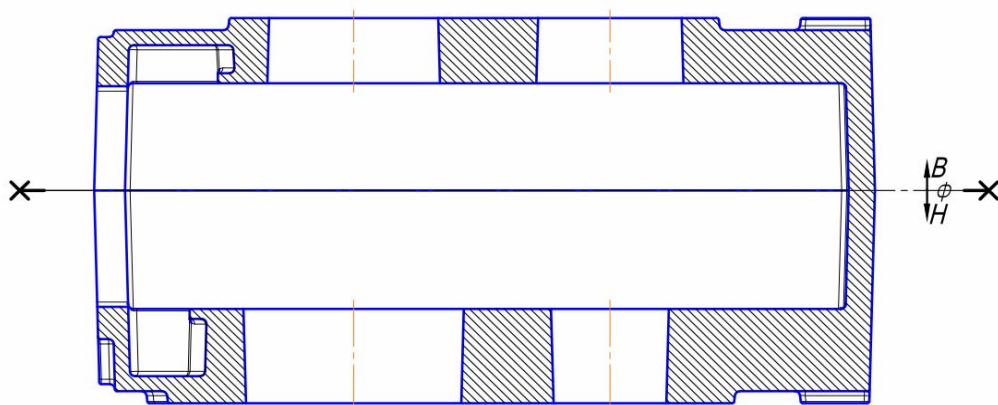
Схема виливка з площиною рознімання форми і його положення у формі при заливанні
